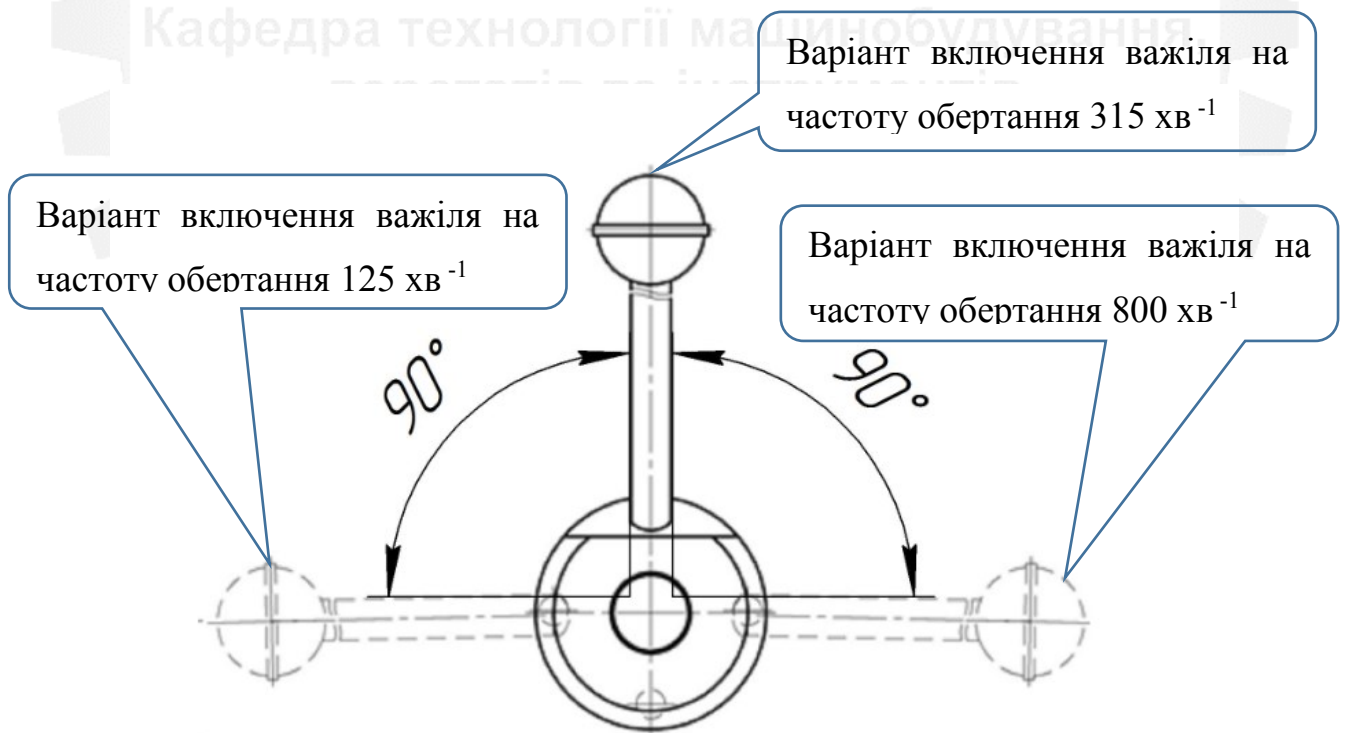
Положення важеля для блоків з трьома зубчастими колесами
